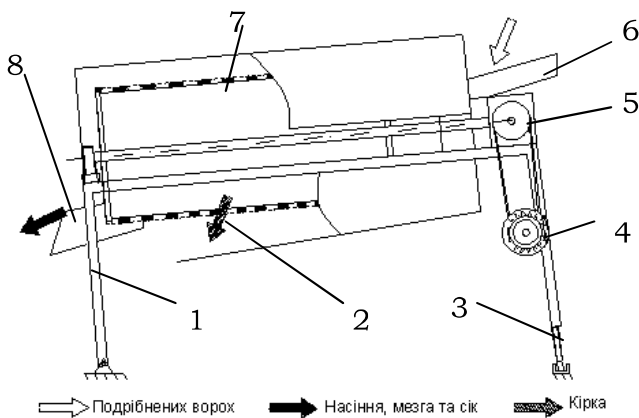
Конструктивно-технологічна схема циліндричного сепаратора
